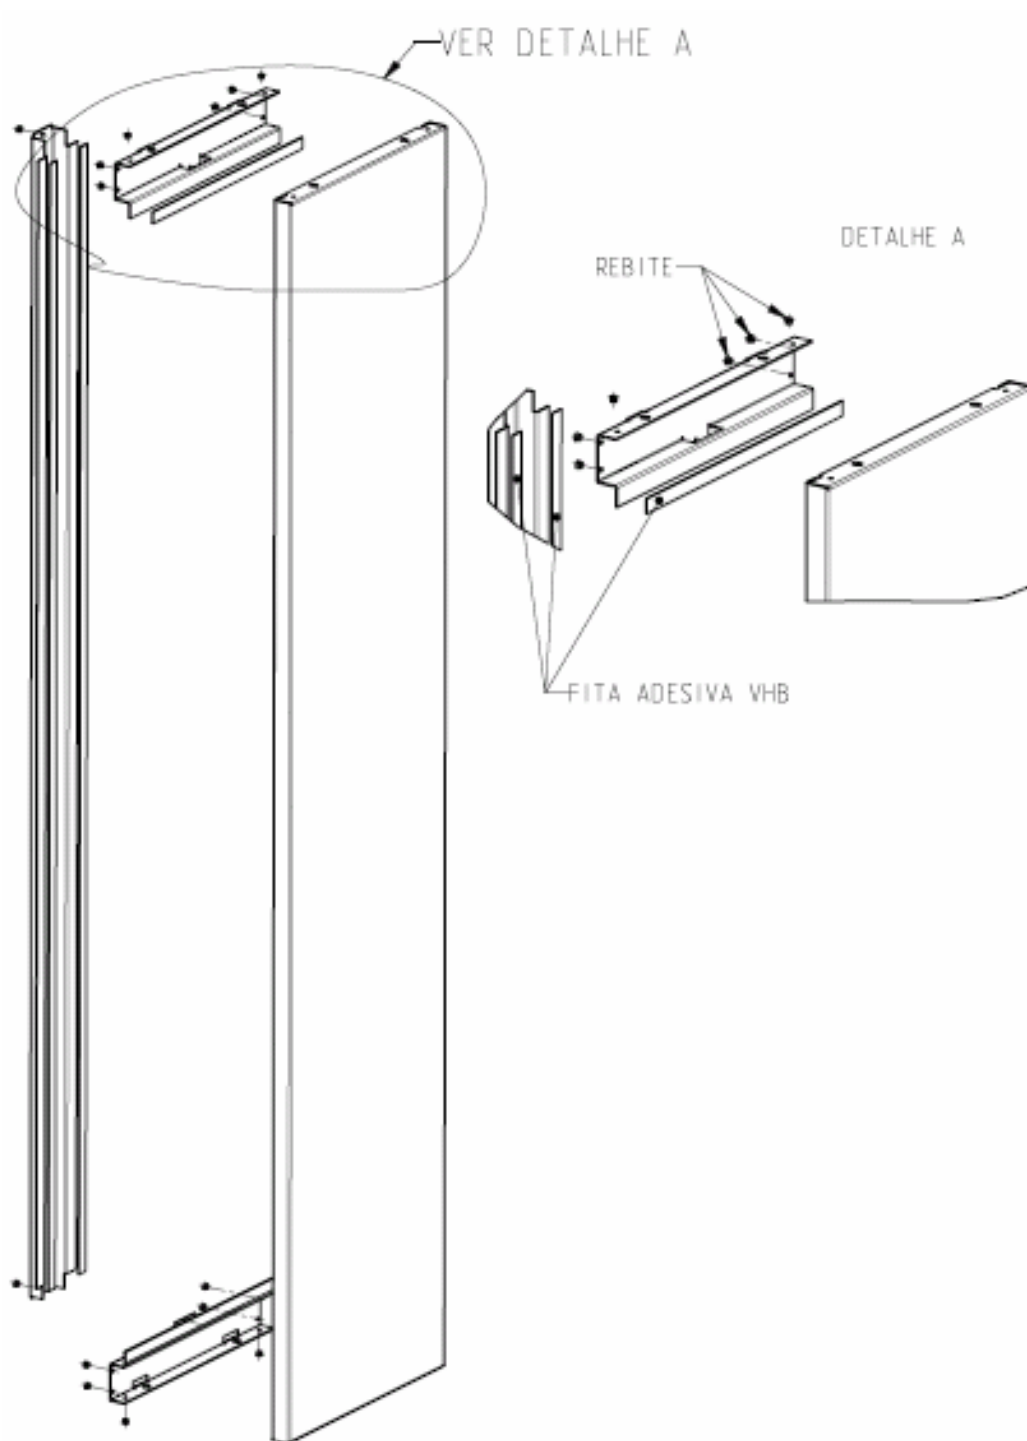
Detalhes da montagem dos componentes de um conjunto painel colado.
